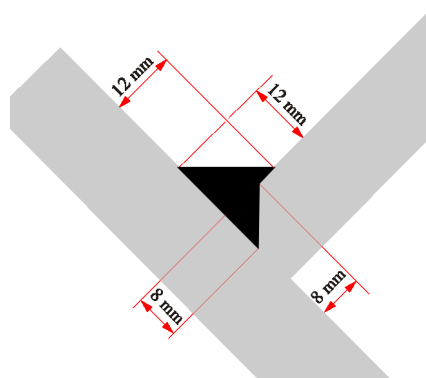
3132-52-01000P020 激振室腹板内筒环焊缝焊接尺寸示意图
